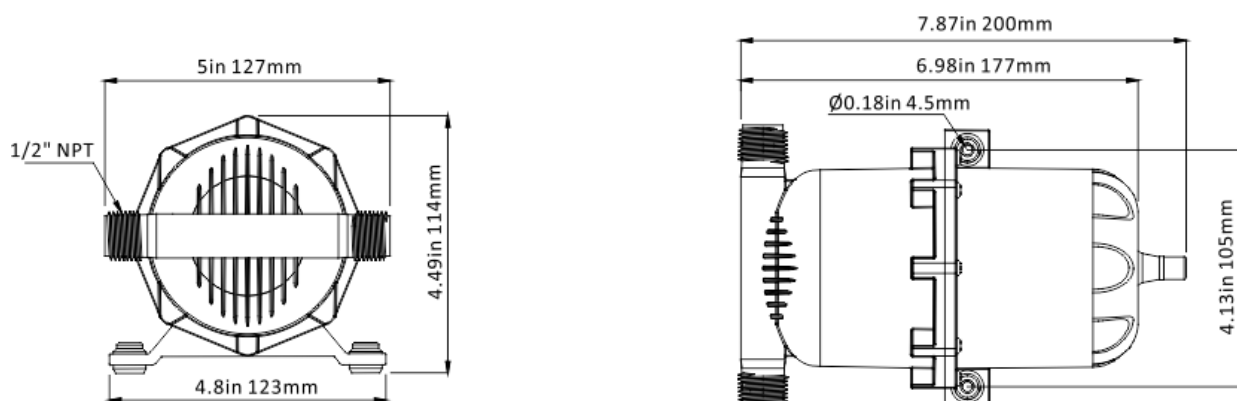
SFAT-075-125-01, габаритные размеры
